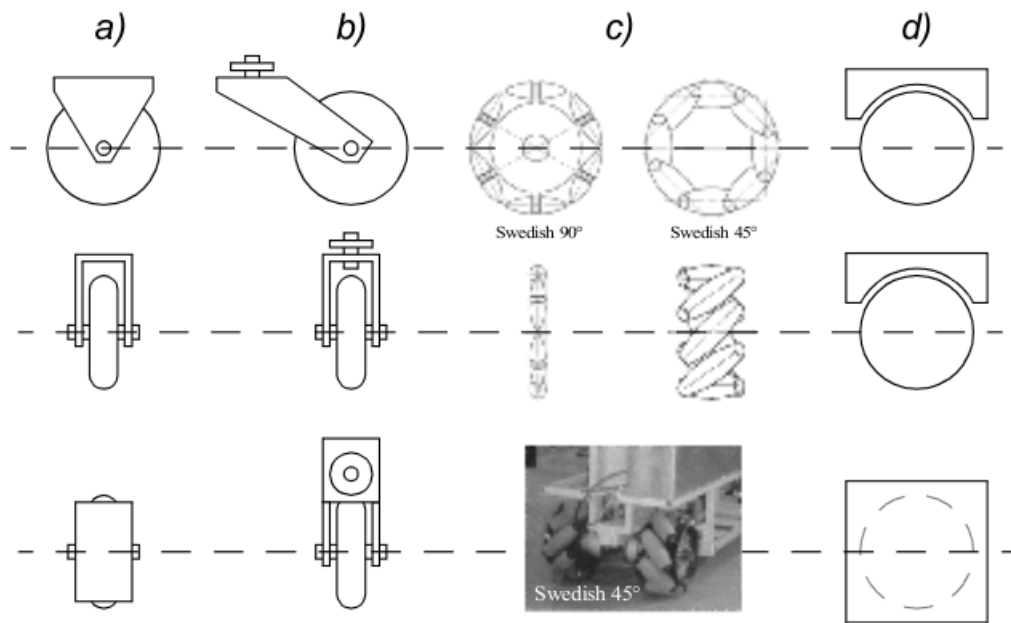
Quatro tipos básicos de roda. (a) Roda padrão. (b) Roda castor. (c) Roda sueca. (d) Bola ou roda esférica [?].
